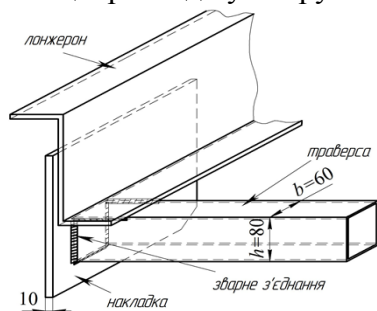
Схема зварного з'єднання поперечини з лонжероном
